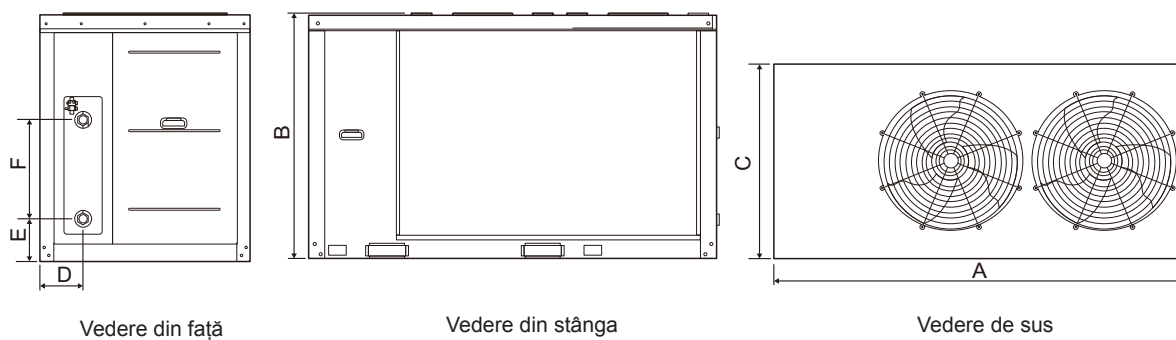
Schema dimensională a KEM-60 DRS4.1
